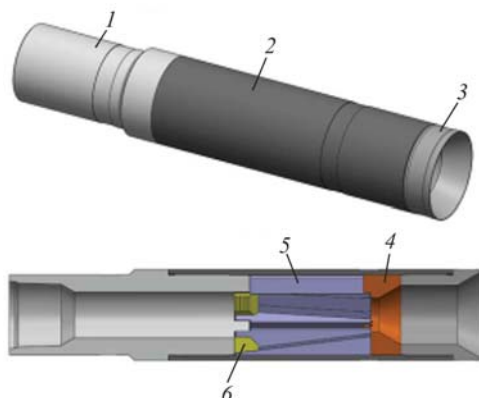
Общий вид универсального ловителя: 1 – переводник; 2 – корпус; 3 – воронка; 4 – фиксатор; 5 – вставка; 6 – плашка
